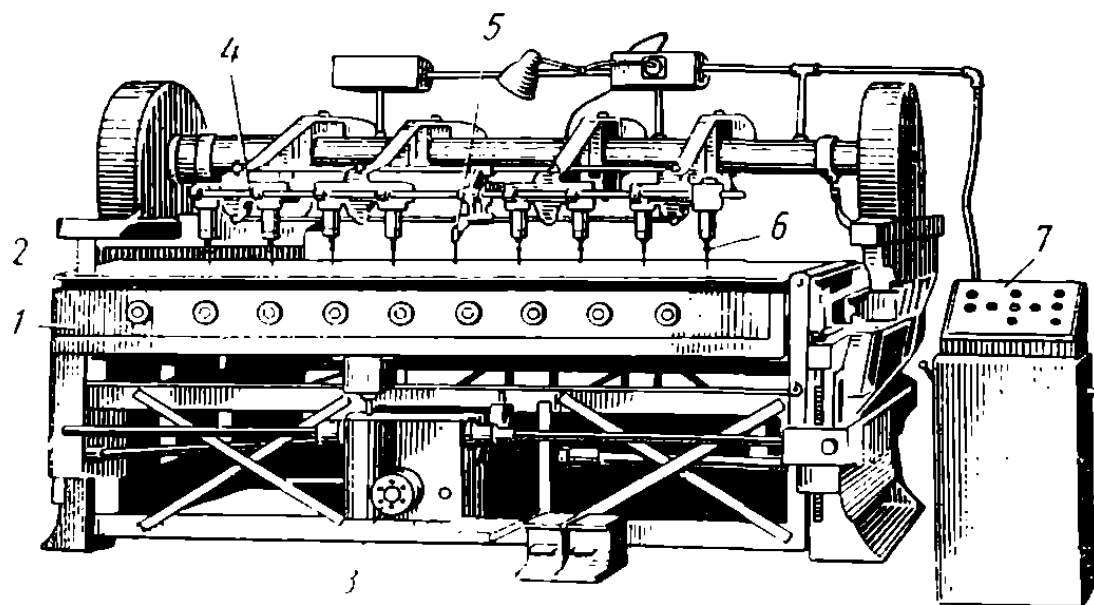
Многошпиндельный копировально-фрезерный станок:
